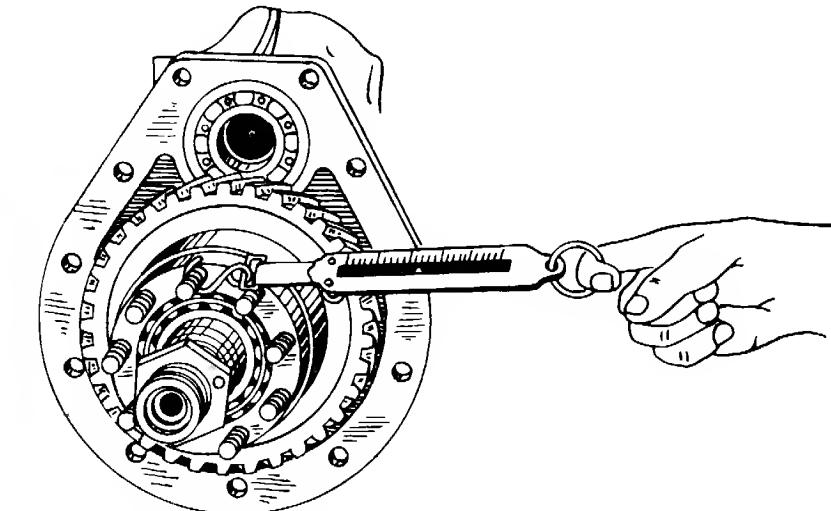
Проверка затяжки подшипников ступицы колеса с помощью динамометра
